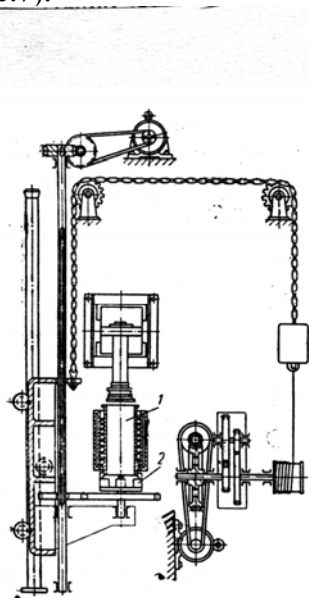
Кінематична схема верстата для поверхневого гартування гільз
